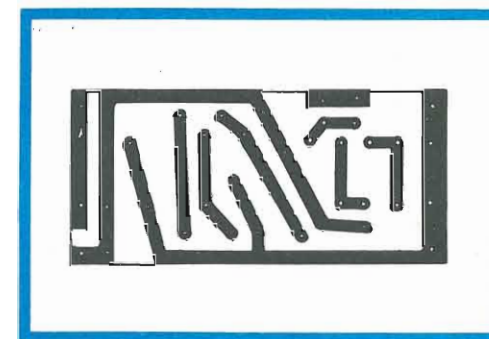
Circuito stampato dell'amplificatore di B.F. visto dal lato delle saldature — scala 1:1.
